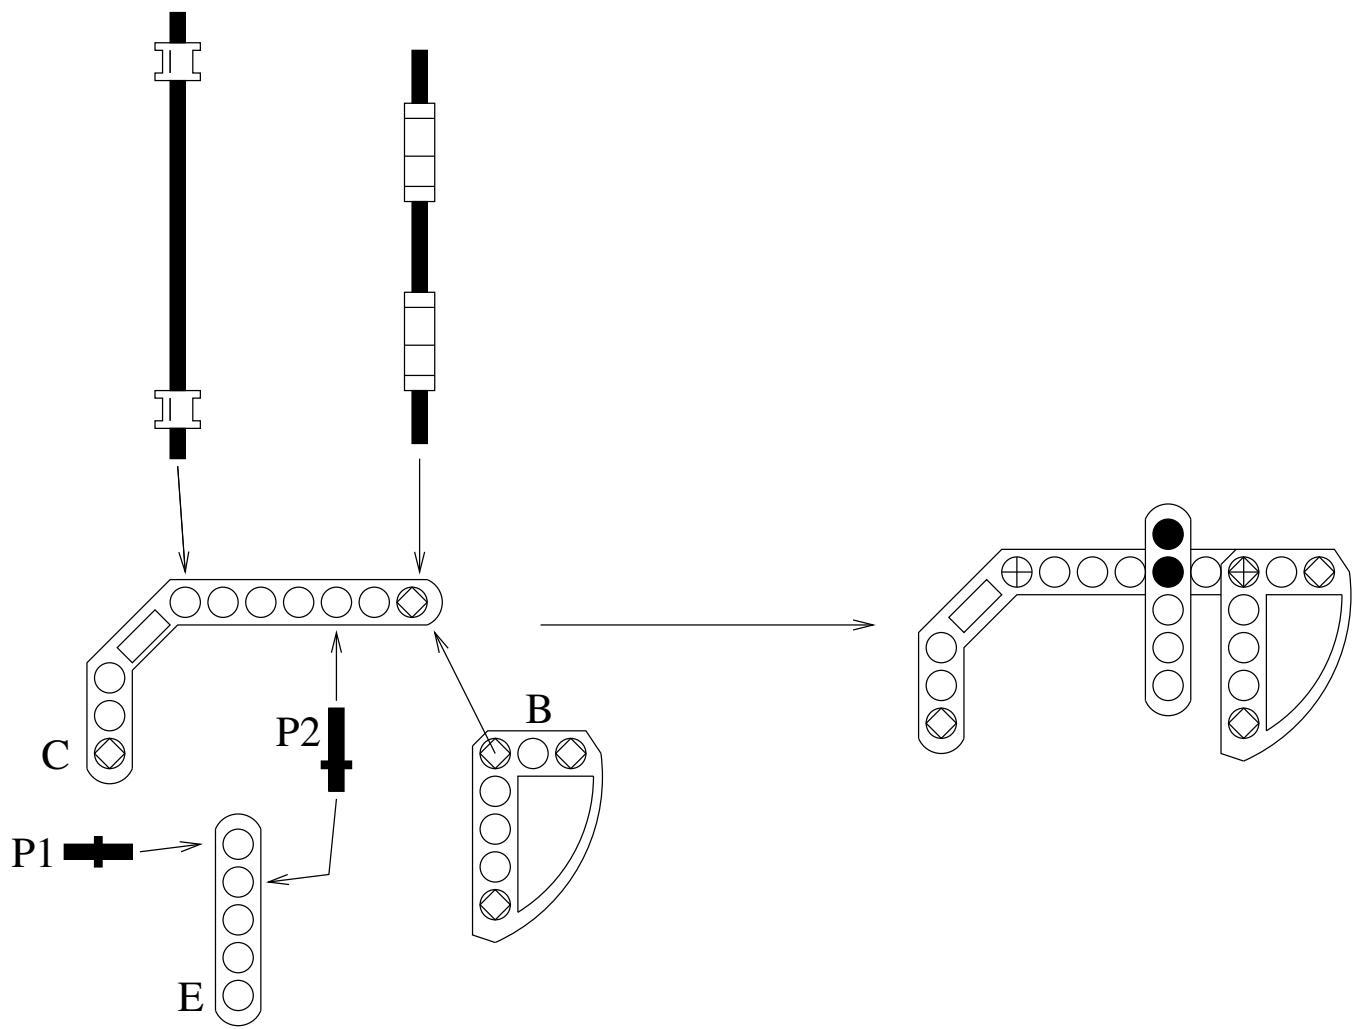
Estructura final del lateral. El otro lateral será igual, teniendo en cuenta que las piezas E y B, estarán situadas en el exterior y la pieza C en el interior.
